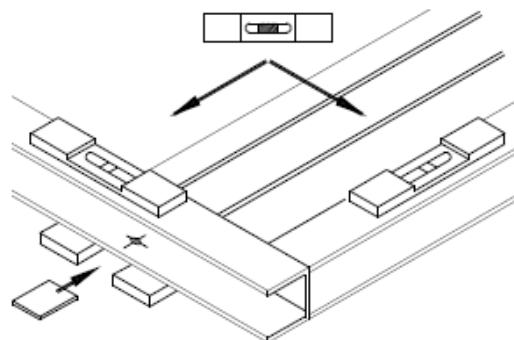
(установка плиты основания на подкладки, находящиеся рядом с фундаментными болтами)
